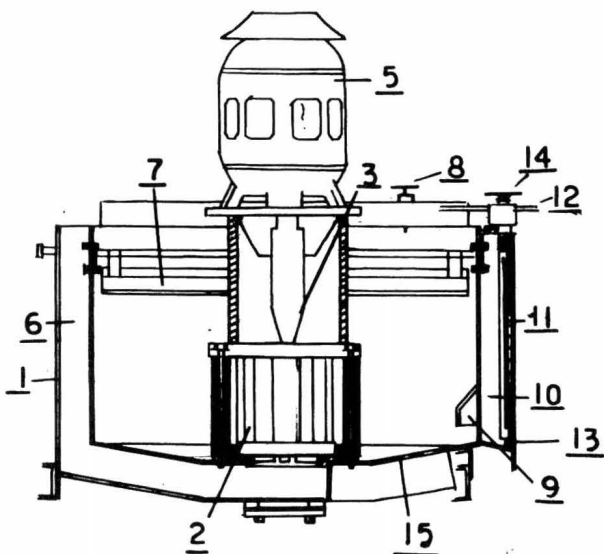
MAQUINA CON ROTOR Y ESTATOR
